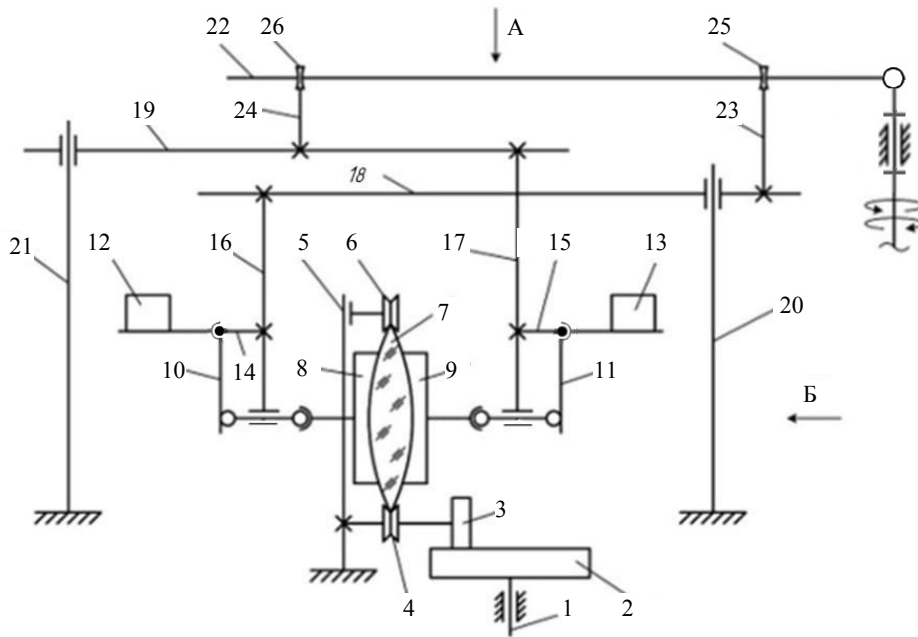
Кинематическая схема устройства для двусторонней обработки линз
